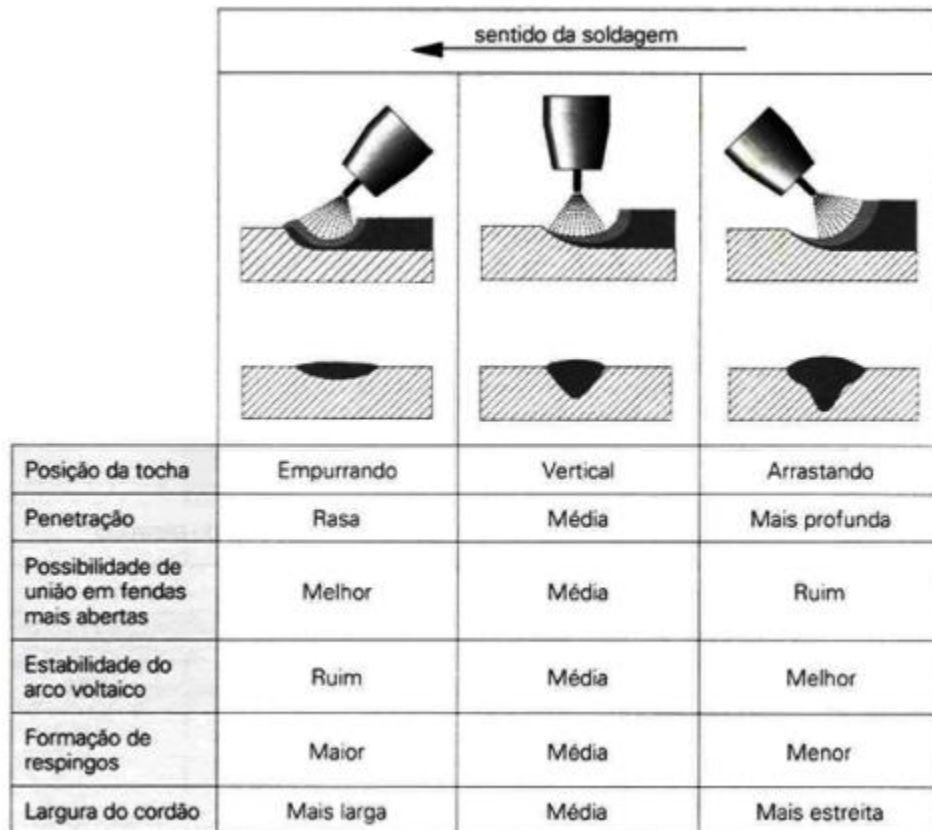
Efeito da posição do eletrodo e técnica de soldagem <sup>(68)</sup>.
